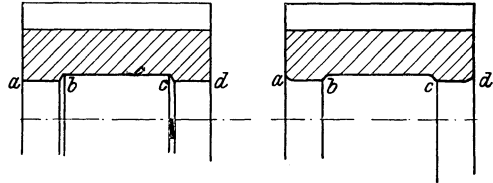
Falsch gedrehter und richtig gedrehter Fräser.
